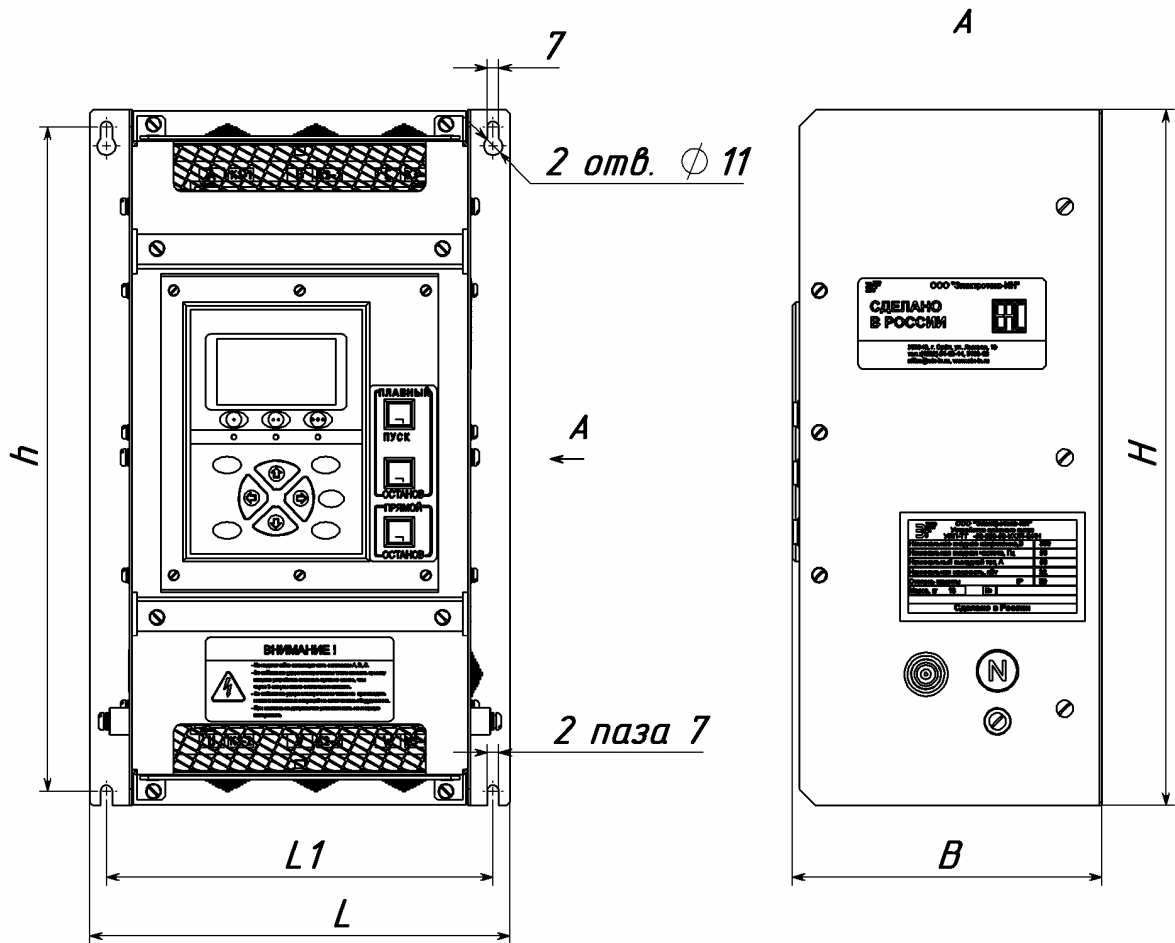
а - Габаритные и установочные размеры УПП 18,5-30 кВт
